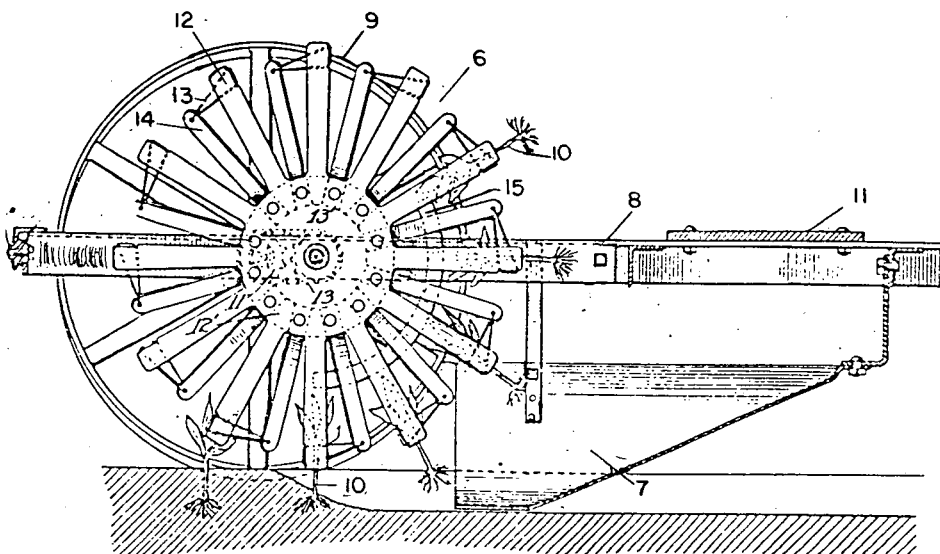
Detalhe do conjunto plantador |5|.
